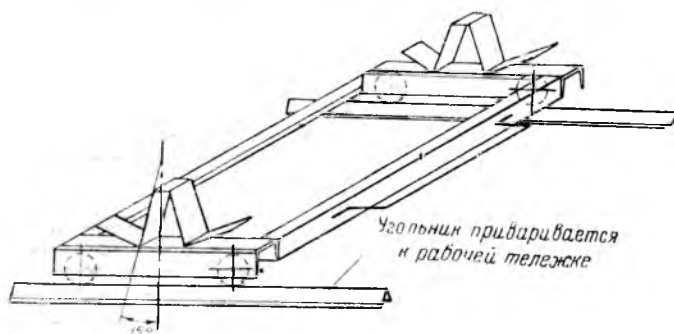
Каретка рабочей тележки шпалооправочного станка ШОСД-7
